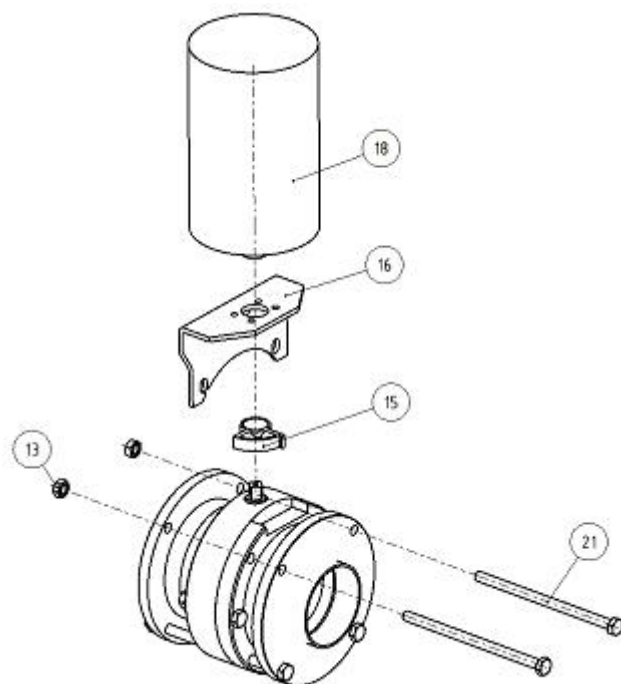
Kugelventil-ZF mit pneumatischem Antrieb
